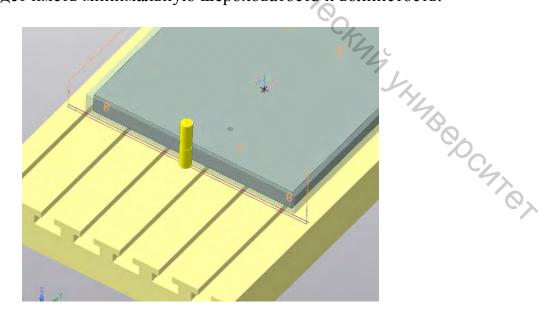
Визуализация процесса фрезерования габаритов заготовки
